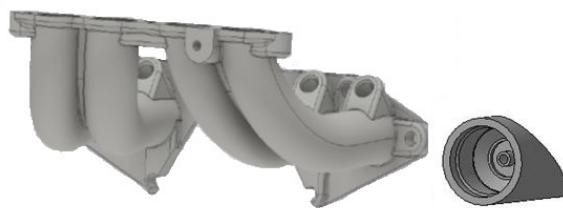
3D-модели впускного коллектора и адаптера для форсунки
